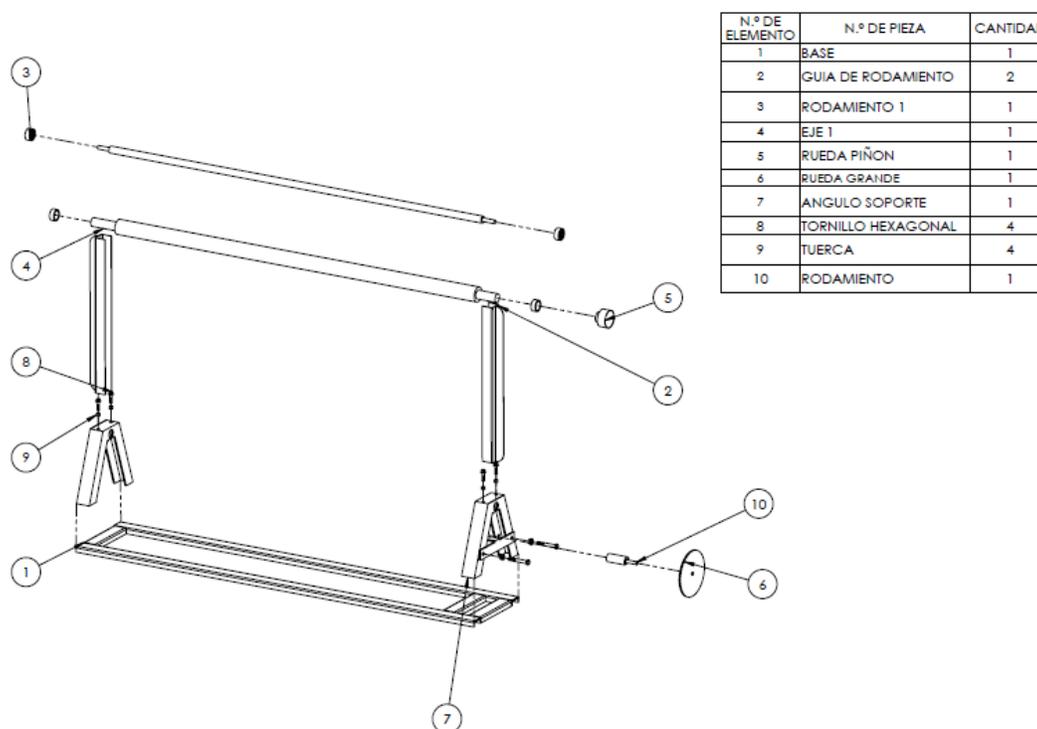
Despiece del diseño del soporte complementario de la rebanadora
